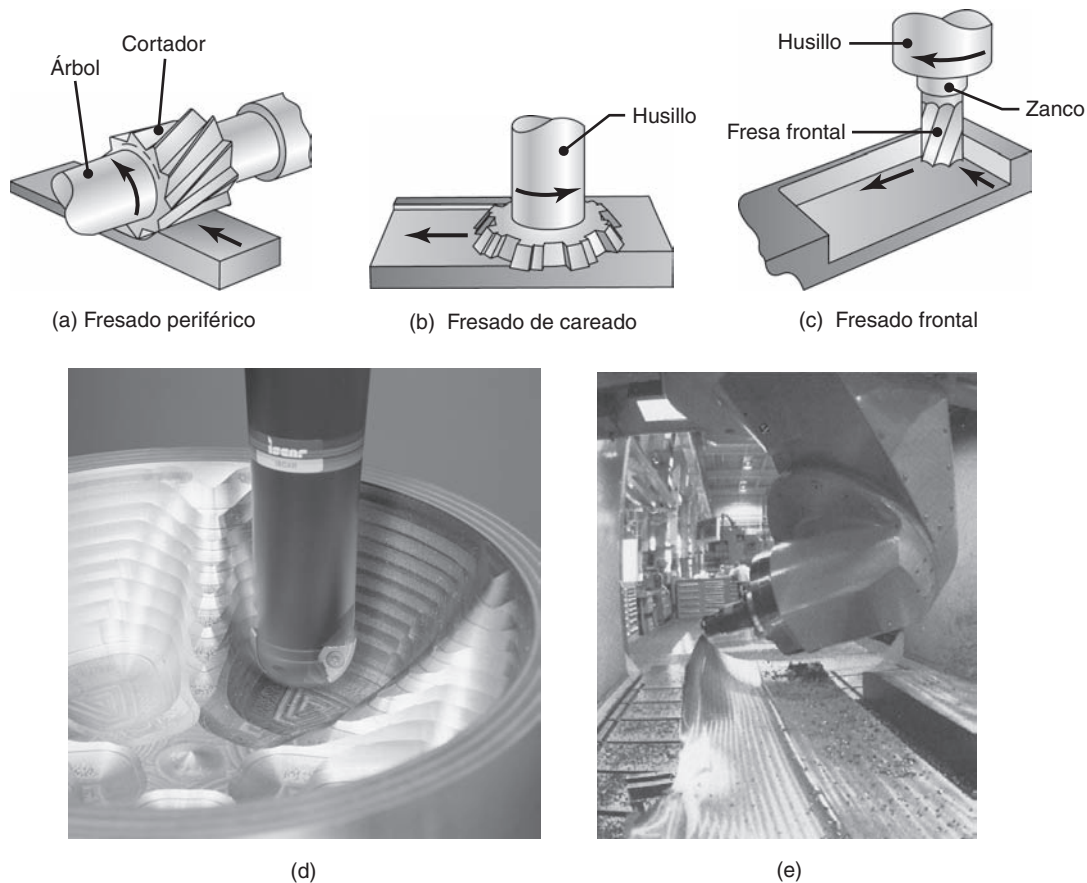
Algunos tipos básicos de cortadores y operaciones de fresado. (a) Fresado periférico. (b) Fresado de careado o refrentado. (c) Fresado frontal. (d) Fresa de punta esférica con insertos indexables con cubierta de carburo maquinando una cavidad en una matriz. (e) Fresado de una superficie esculpida con una fresa frontal, utilizando una máquina de control numérico de cinco ejes. Fuente: (d) Cortesía de Iscar Metals, Inc. (e) Cortesía de The Ingersoll Milling Machine Co.
